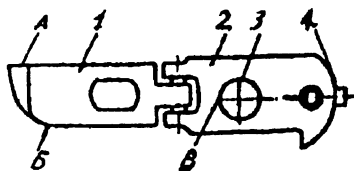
Устройство защелки шпульного колпачка (машина 2М кл. ПМЗ):
